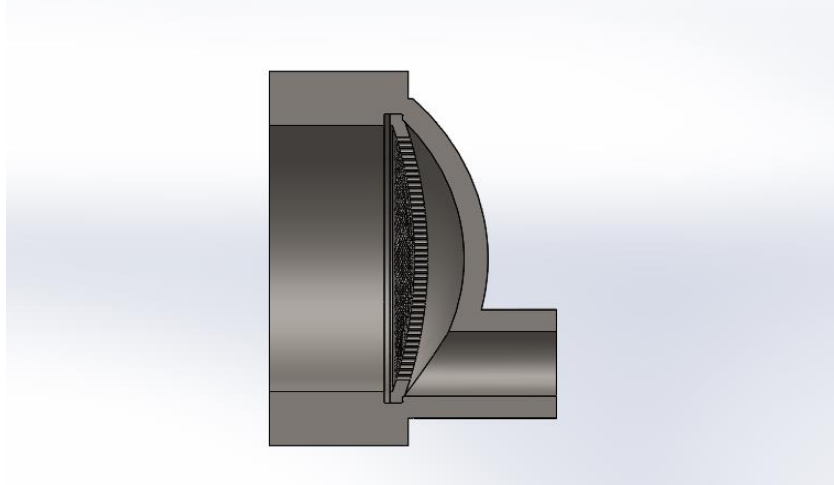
Ensamblaje del plato y la caja de válvulas. Fuente: elaboración propia
